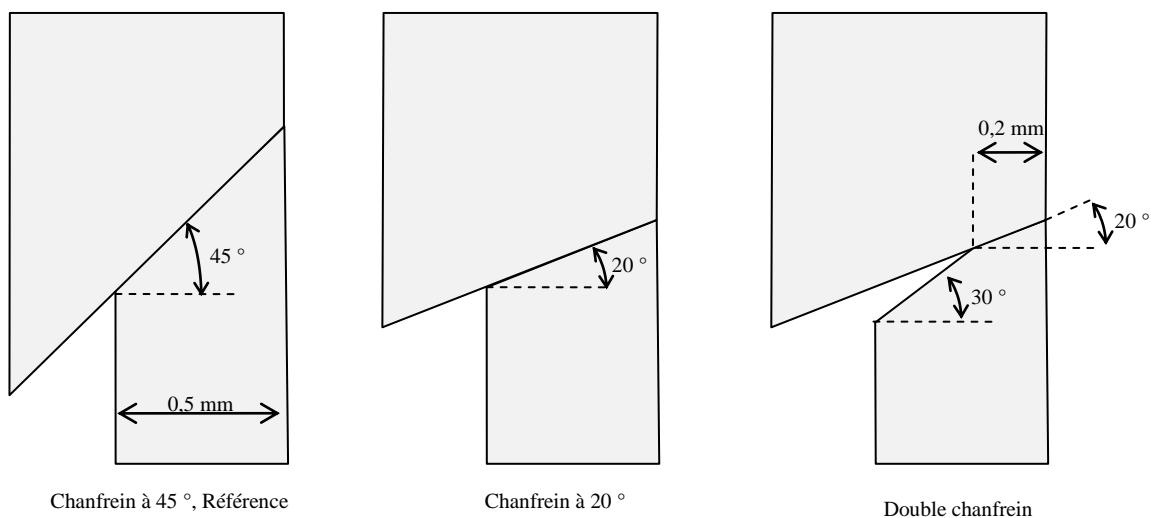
Dimensions de différentes géométries de contact étudiées dans le but d'éviter le manque de soudage sur l'extérieur du joint
